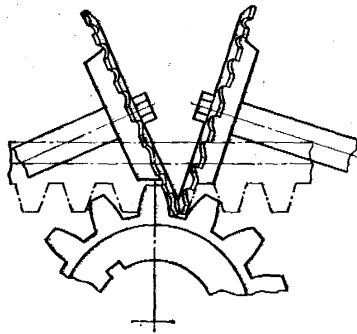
Схема фрезерования двумя дисковыми фрезами методом обкатывания
